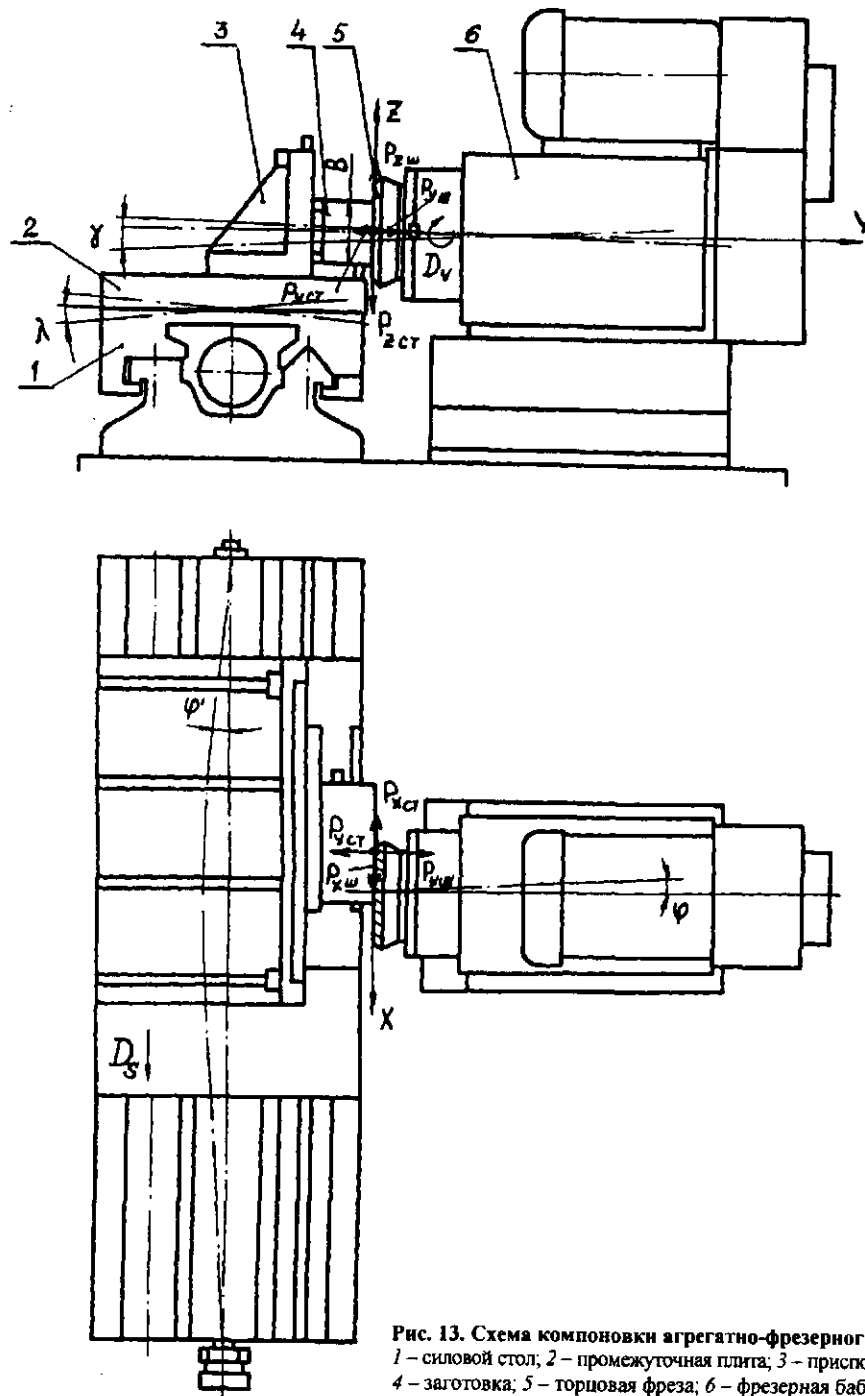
Схема компоновки агрегатно-фрезерного станка: 1 – силовой стол; 2 – промежуточная плита; 3 – приспособление; 4 – заготовка; 5 – торцовая фреза; 6 – фрезерная бабка
